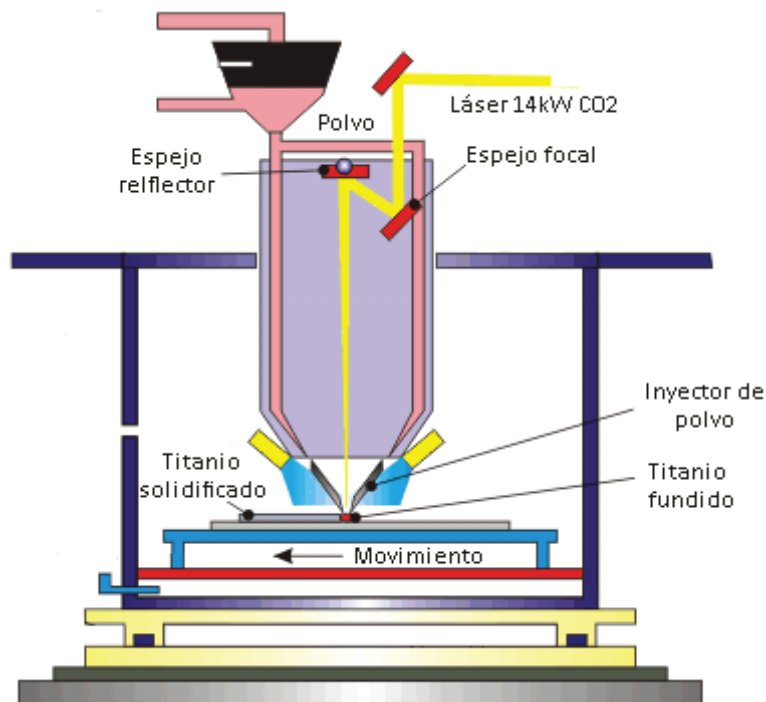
Deposición de polvo mediante laserforming [25]
